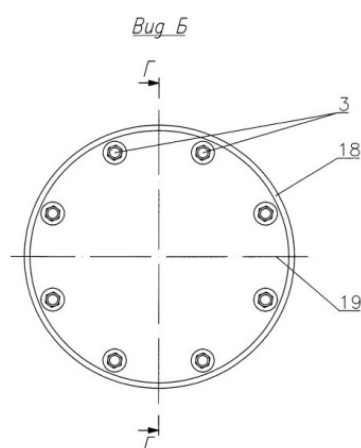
Взрывная камера в сборе с дном и крышкой, вид Б на рис. 8, вид сверху
